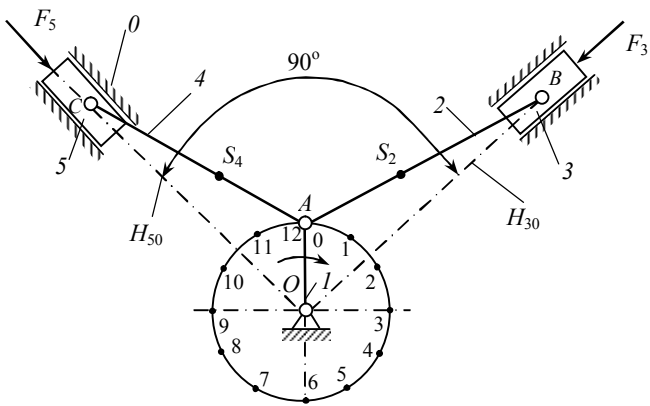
Схема механизма V-образного двигателя аэродромного пускового агрегата
